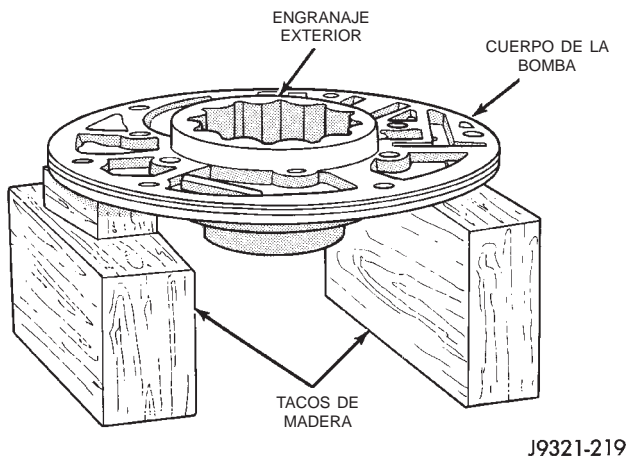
Sujeción de la bomba e instalación del engranaje exterior
